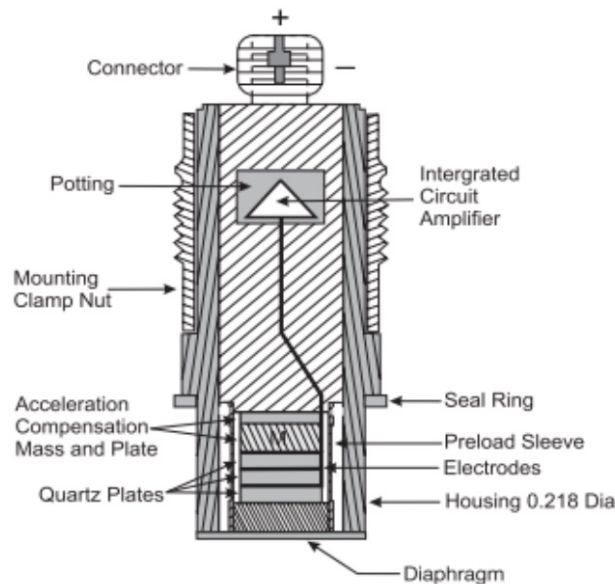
Vue en coupe d'un capteur développé par la société PCB [38]
